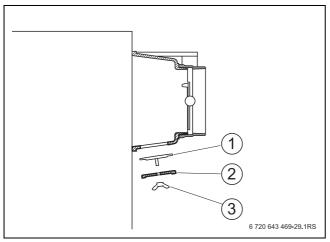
Крышка люка для чистки на сборном коллекторе дымовых газов
